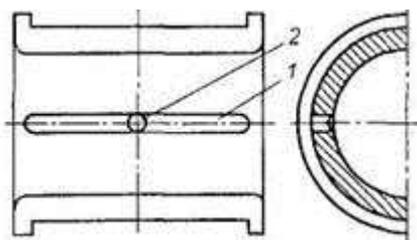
Вкладыш: 1 — канавка; 2 — отверстие для подвода смазки
